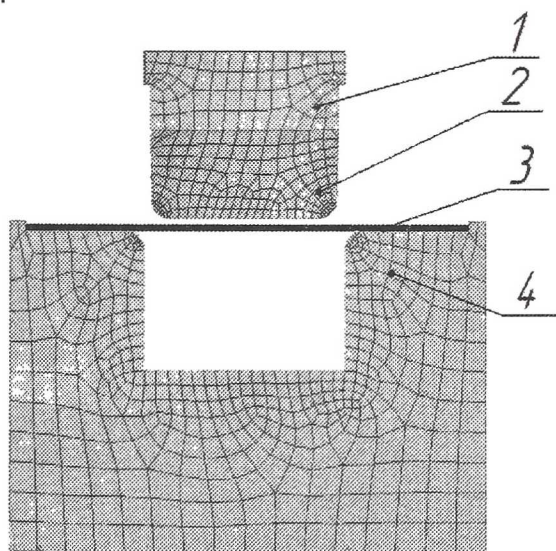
Конечно-элементная модель: 1 – корпус; 2 – полиуретановый пуансон; 3 – заготовка; 4 – матрица
